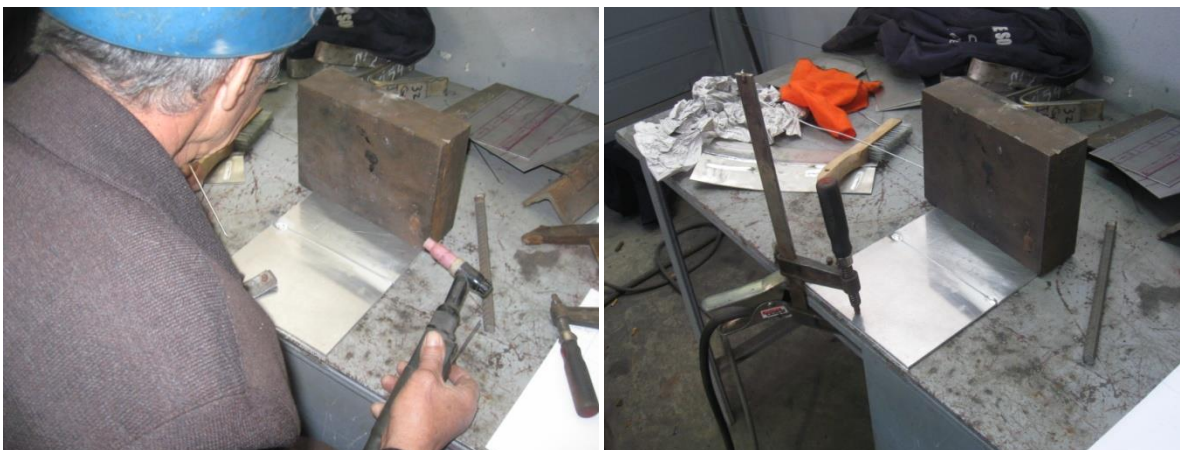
Premières étapes du procédé de soudage TIG
